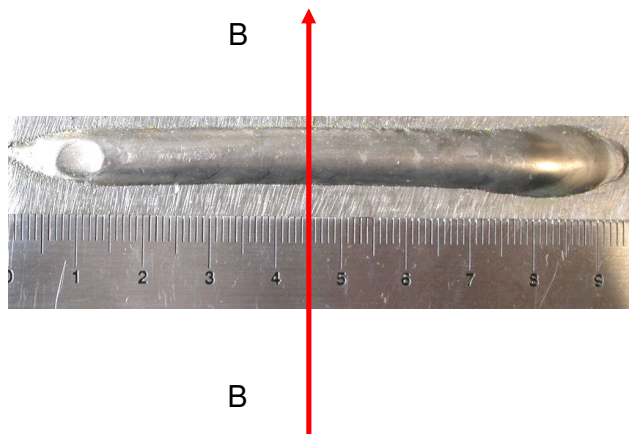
Cordão de solda cortado transversalmente, através do plano BB.
